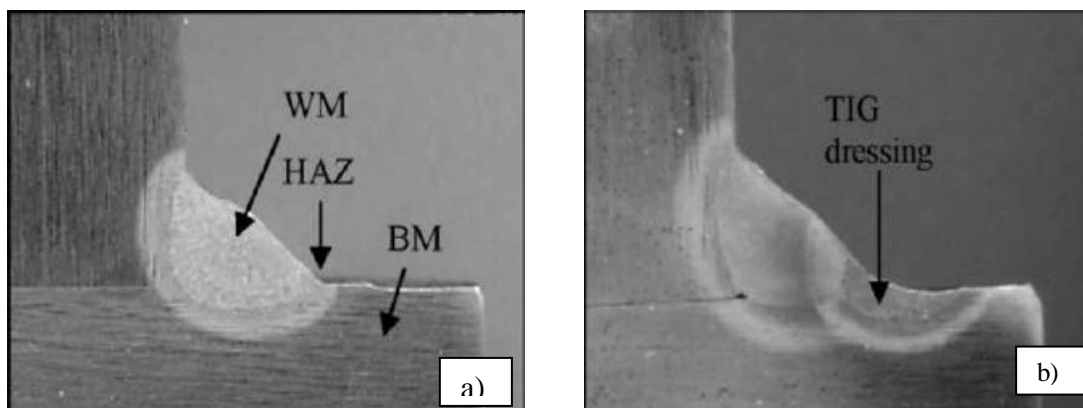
Macros de juntas soldadas a) como soldado b) TIG dressed
